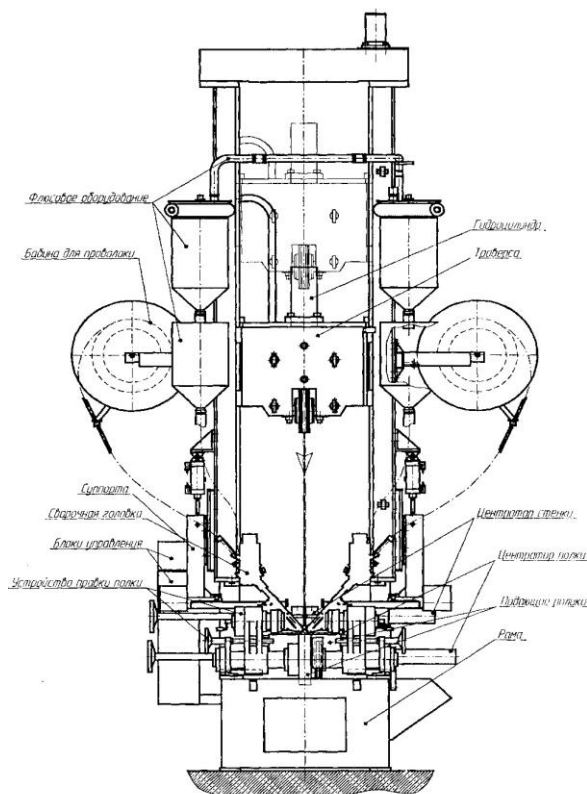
Установка для сварки балок ИТ 258 В А (фронтальная проекция)
